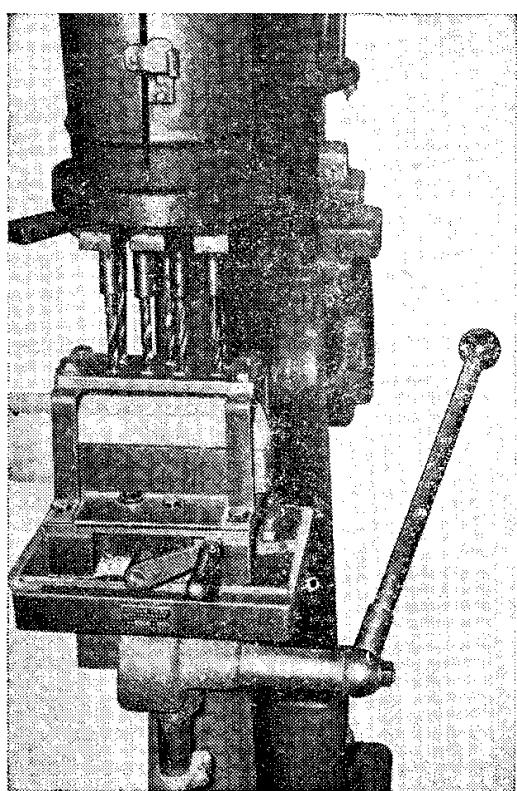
Сверление отверстий в головках под колковые механизмы по кондуктору на многошпиндельном сверлильном станке
